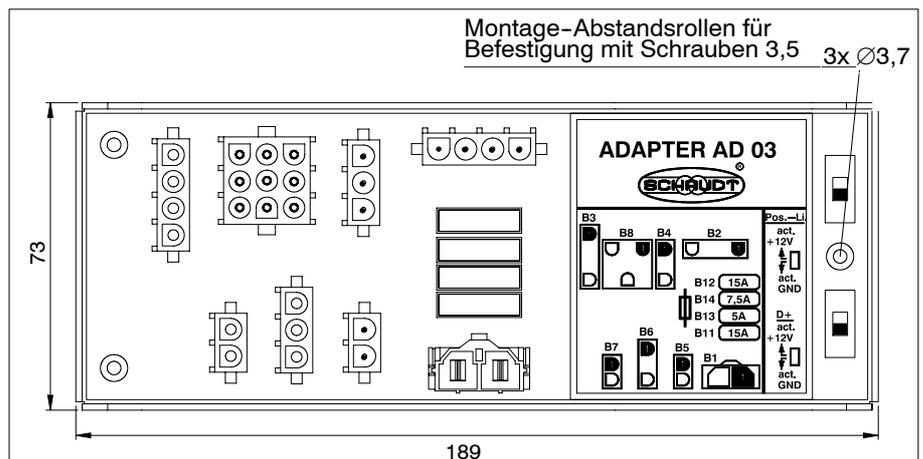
Maßbild Adapter AD 03 (Abmessungen in mm)
